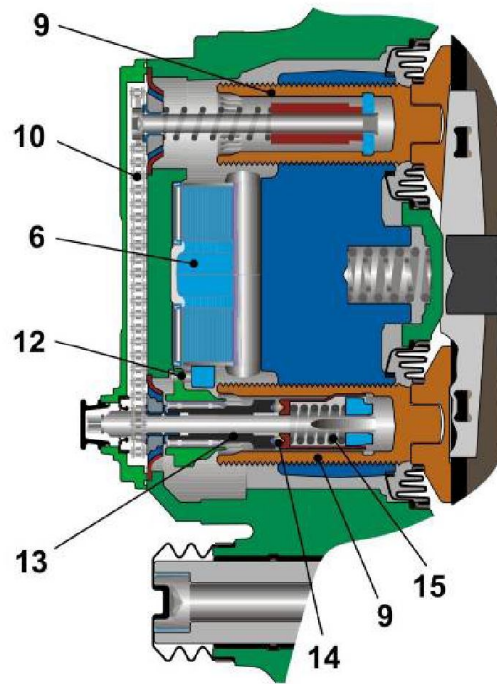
Пристрій автоматичного регулювання зазору:
